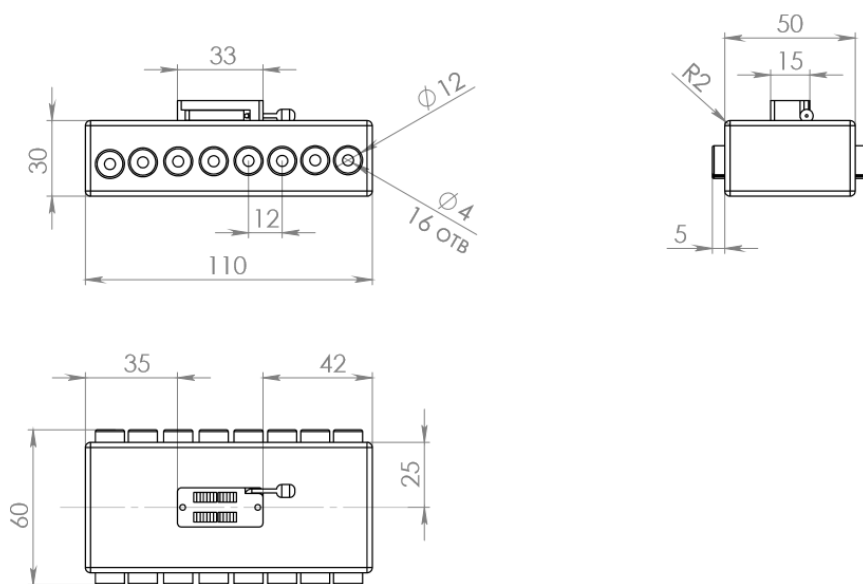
86. Сборочный чертеж оснастки для входного контроля
